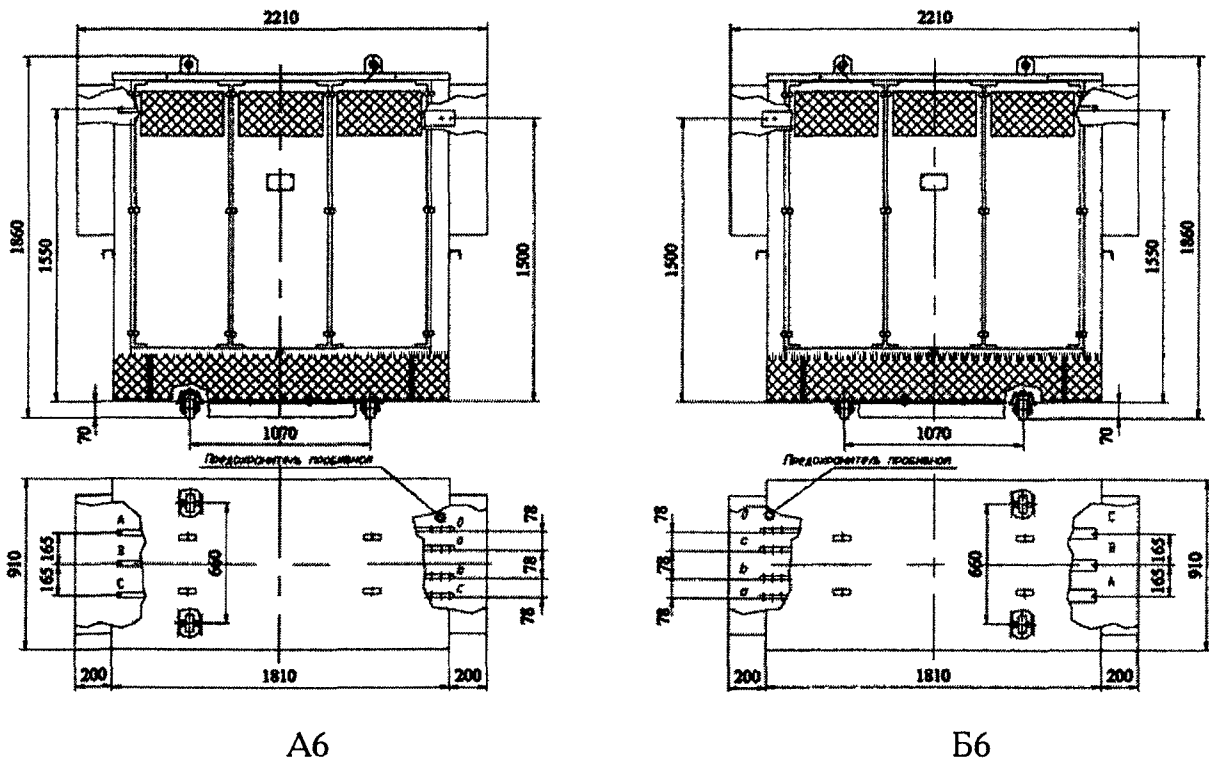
Габаритные, установочные, присоединительные размеры трансформатора ТСЗФ-1000/10 УЗ (сторона подключения: А6 - левая, Б6 - правая)
